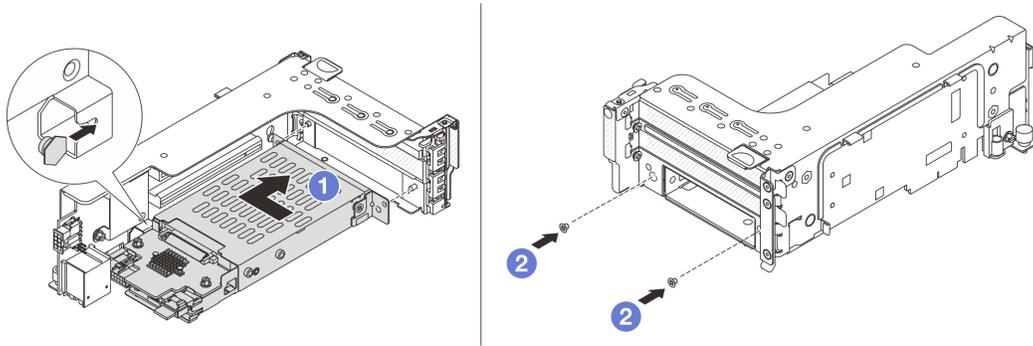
Installation du boîtier d'unités de disque dur 7 mm
